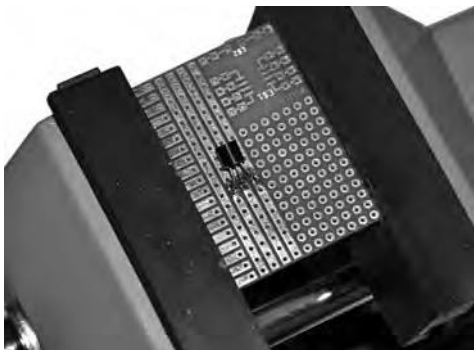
Con la pompa di dissaldatura, la saldatura deve essere completamente estratta da tutti e tre i punti di saldatura in più passaggi.
